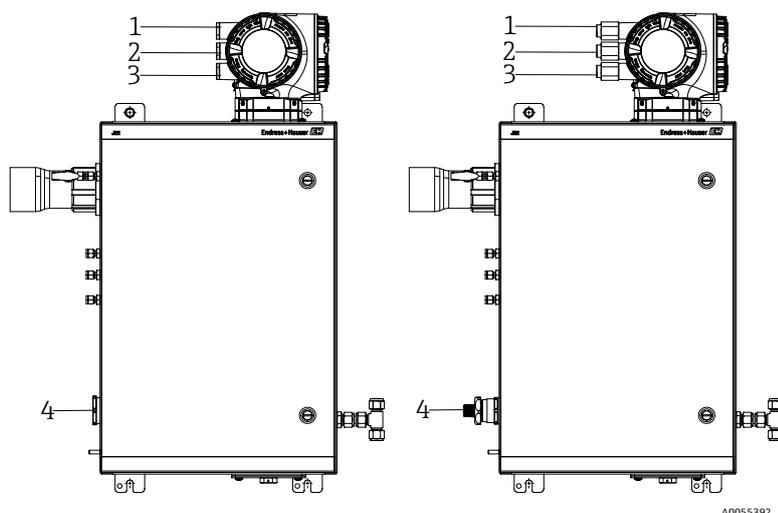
Gewindeeinführungen für J22-Gehäuse für ATEX-Anschlüsse (links) und zöllige Anschlüsse (rechts)
